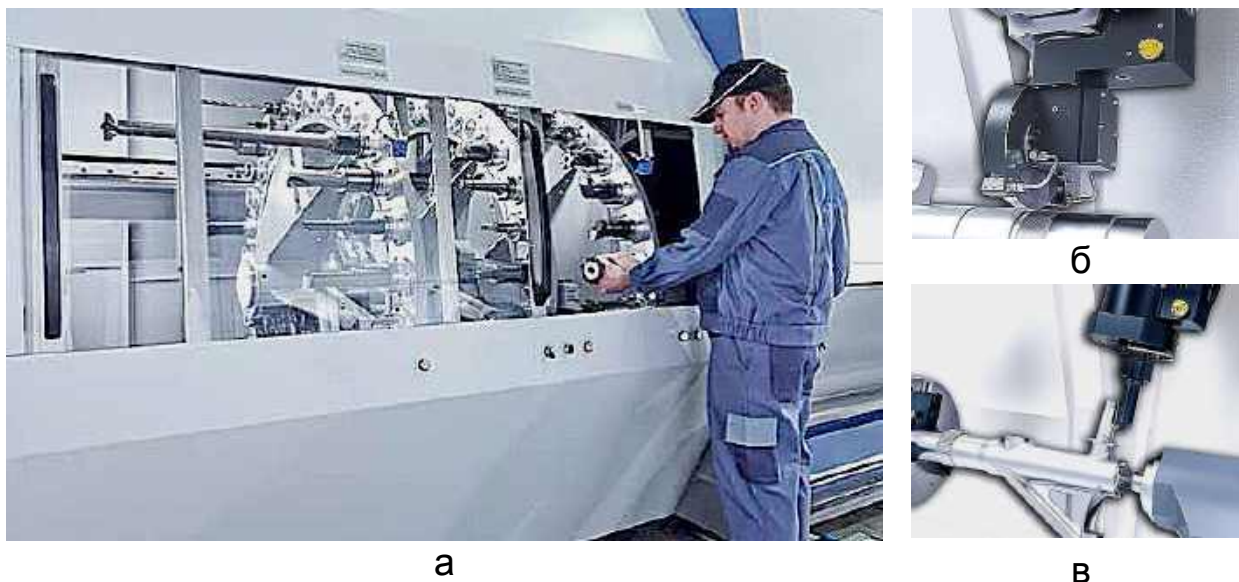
Загальний вигляд трьох дискових інструментальних магазинів (а), шліфувальної (б) та розточувальної (в) насадок верстатів WFL Millturn
